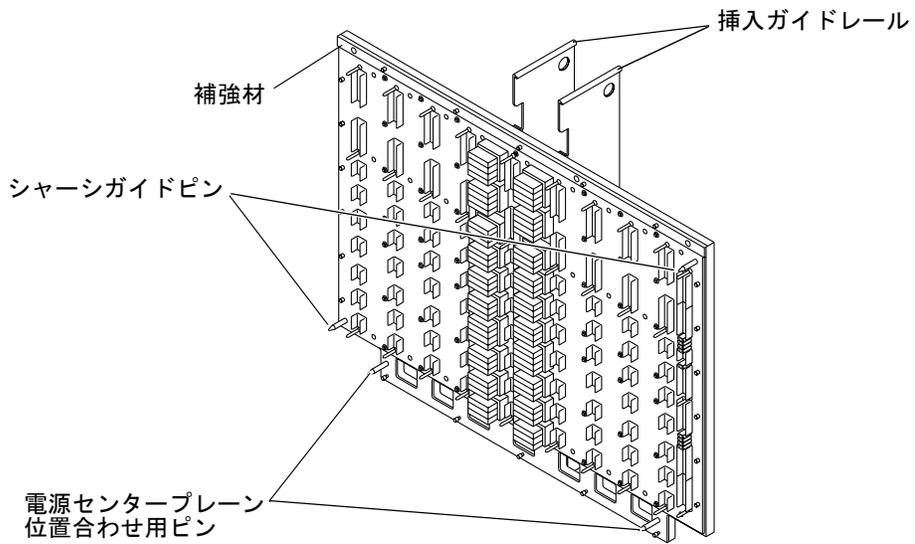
Sun Fireplane interconnect 部品 - 正面図および背面図
